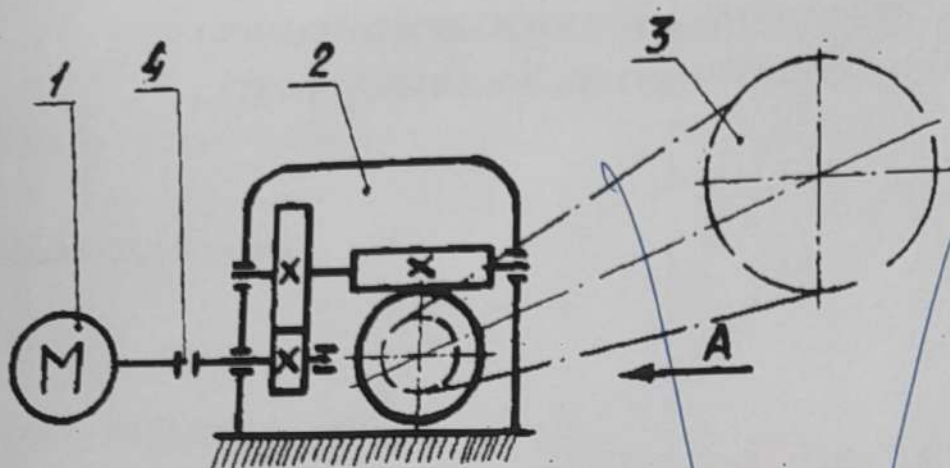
Кинематическая схема привода: 1- электродвигатель; 2- редуктор; 3- гибкая передача; 4 - муфта.
